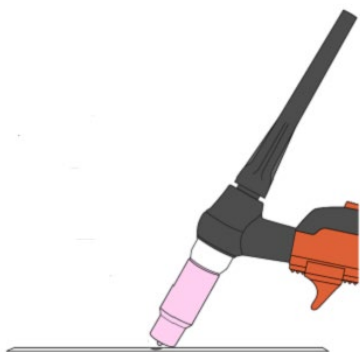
Угол горелки и расстояние при использовании обычной техники сварки. Поверхность листа можно использовать в качестве опоры для газового сопла.
